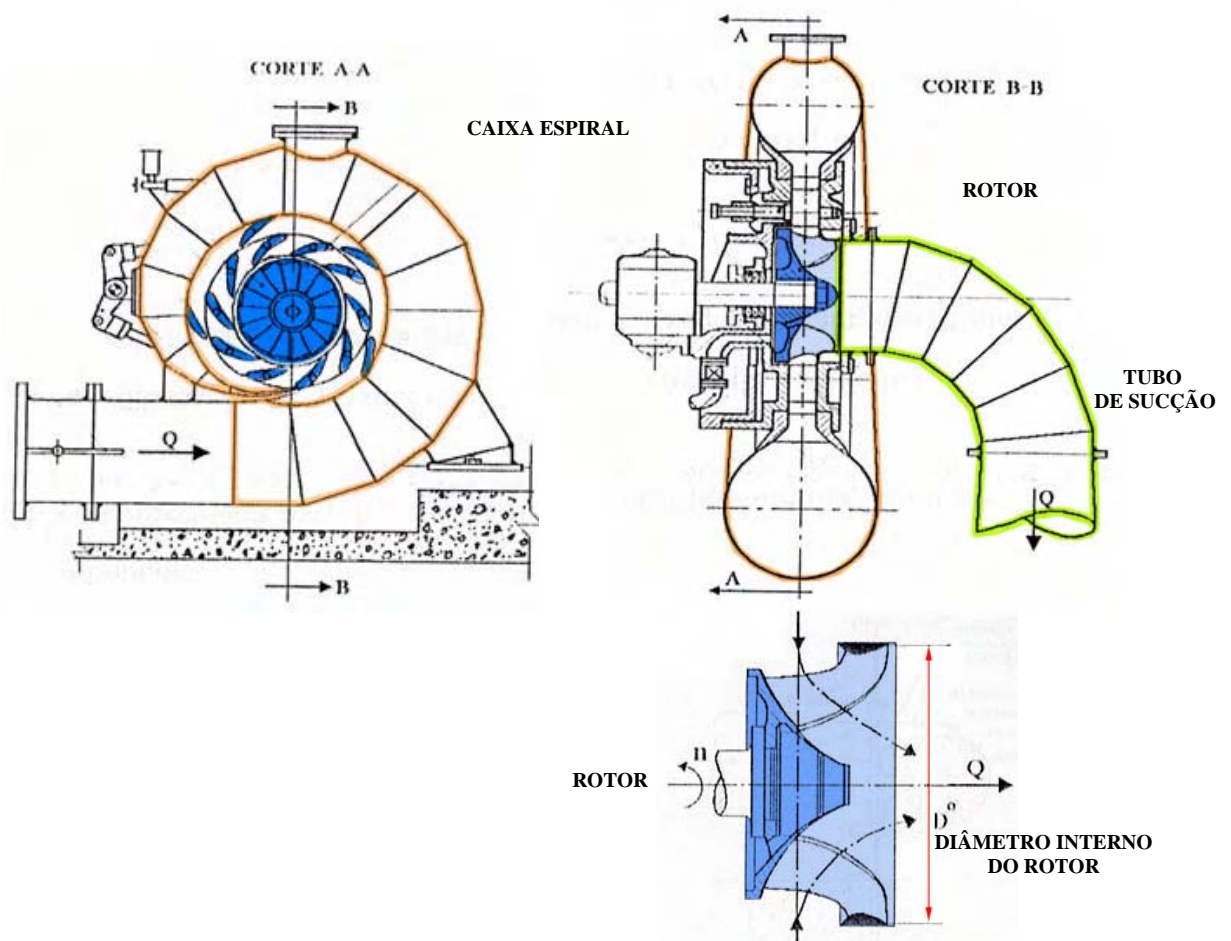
Turbina Francis de eixo horizontal e caixa espiral de chapa soldada, com destaque do rotor
